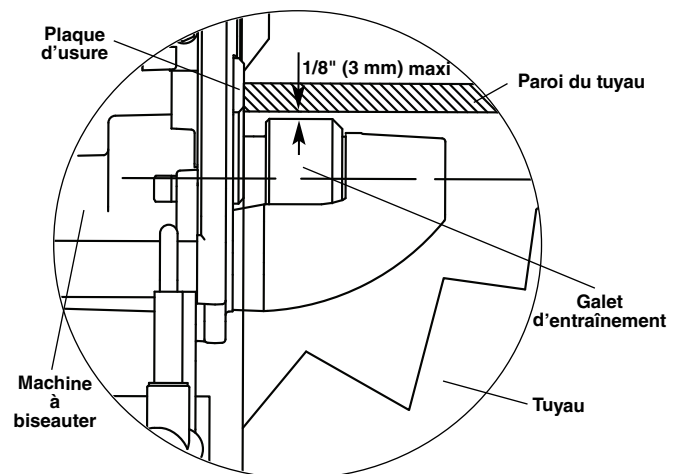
Machine fixe, position du tuyau par rapport au galet d'entraînement (coupe sur tuyau avant engagement)
